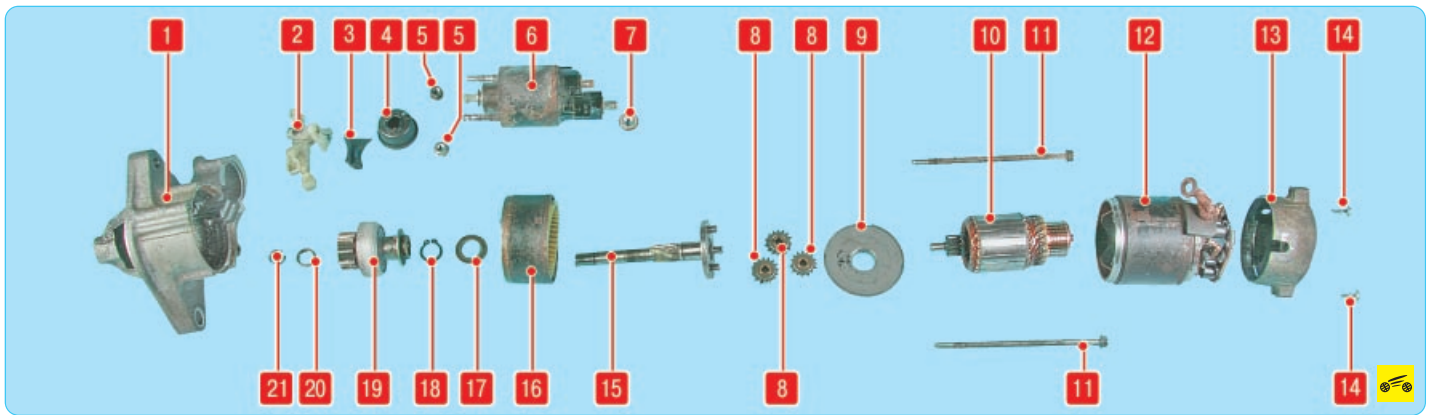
Детали стартера: 1 – корпус стартера; 2 – приводной рычаг; 3 – уплотнитель; 4 – чехол тяги тягового реле; 5 – гайки крепления тягового реле; 6 – тяговое реле в сборе; 7 – гайка крепления силового провода; 8 – планетарные шестерни; 9 – крышка планетарного редуктора; 10 – ротор стартера; 11 – стяжные болты; 12 – корпус статора в сборе с щеткодержателем; 13 – крышка со стороны коллектора стартера; 14 – болты крепления крышки стартера; 15 – вал планетарного механизма; 16 – корпус планетарного механизма; 17 – упорное кольцо планетарного механизма; 18 – стопорное кольцо планетарного механизма; 19 – шестерня привода; 20 – фиксатор стопорного кольца; 21 – пружинное стопорное кольцо
